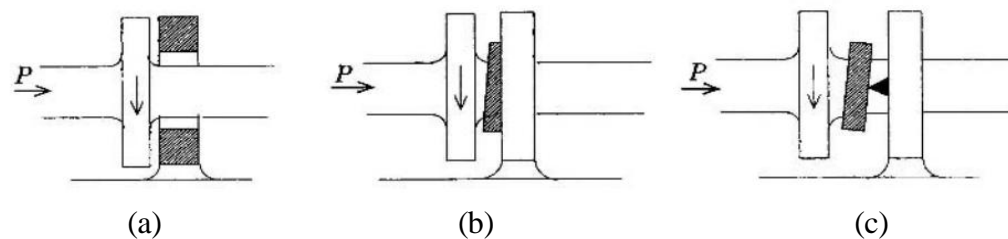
Slider bearing*, (a) *thrust bearing* (b) *journal bearing* [24]
